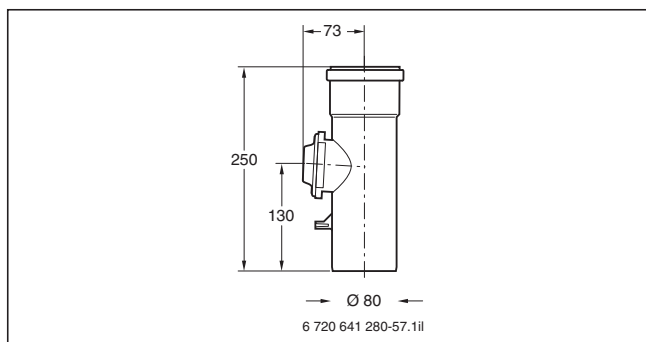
Rohr mit Prüfföffnung (Maße in mm)
